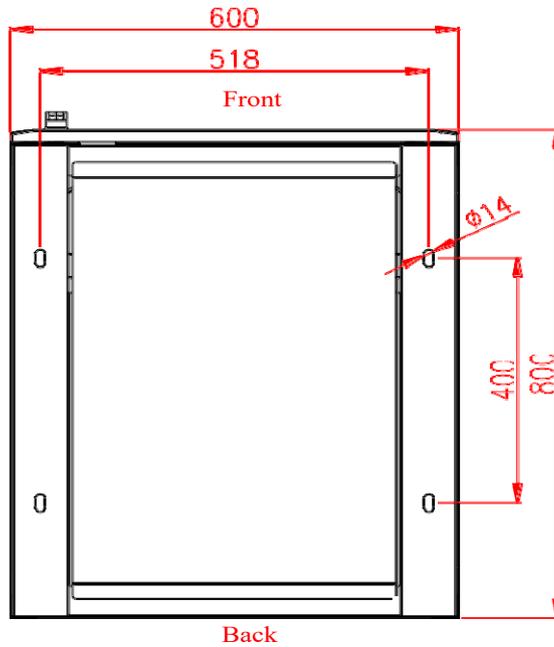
Размер батарейного шкафа для FR-UK 31DL(10~60кВА)
